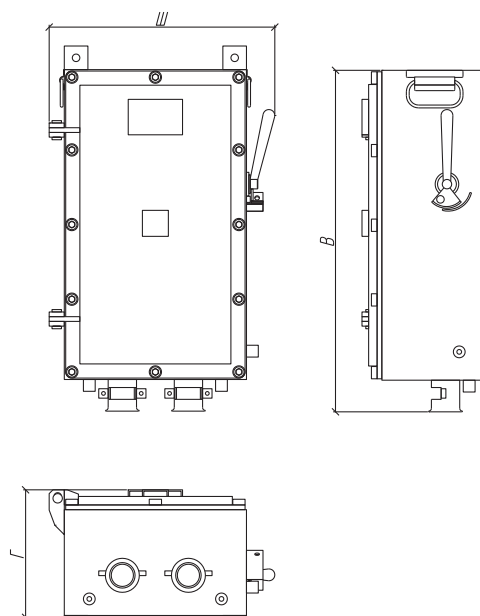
Выключатель автоматический рудничный постоянного тока в корпусе повышенной прочности ВАРП-500-ПП.
